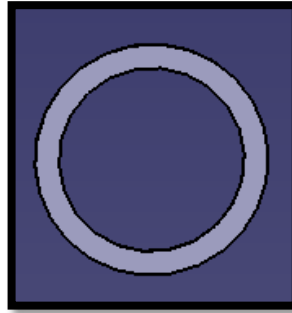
Seat mounting frame 11: Arandela de Dext 48.72 mm y Dint 38.72 mm
